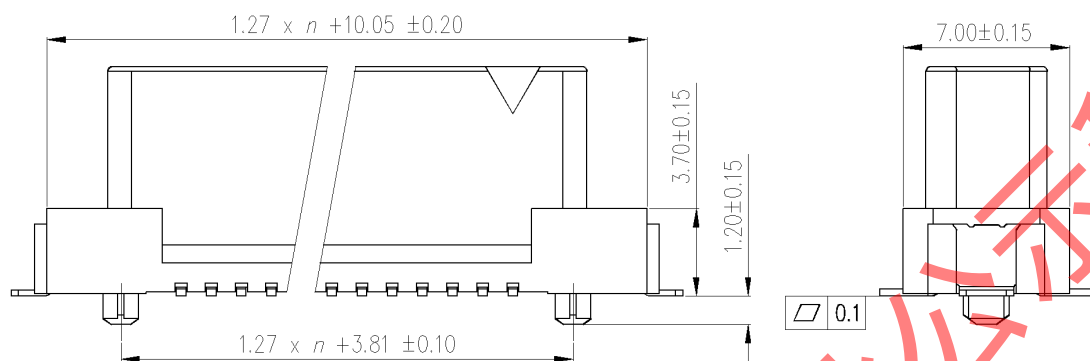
H类型插座 180度贴片焊接式外形尺寸
